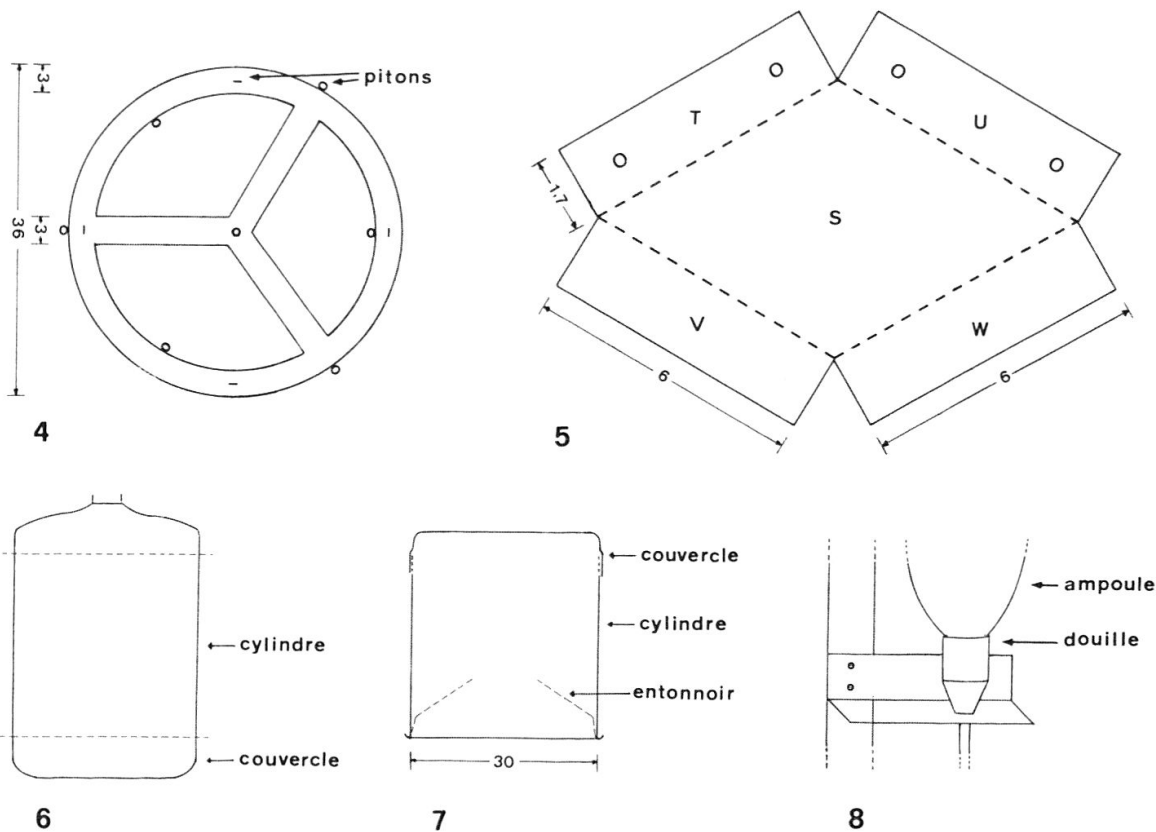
Plan de la roue (4); plan du support basal du mât S (5); découpage du bidon (6); plan du collecteur (7); fixation de la douille au mât (8).
